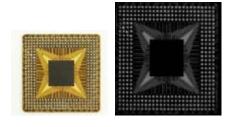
BGA 焊点的成像实例(引自 www.ccs-inc.co.jp)
